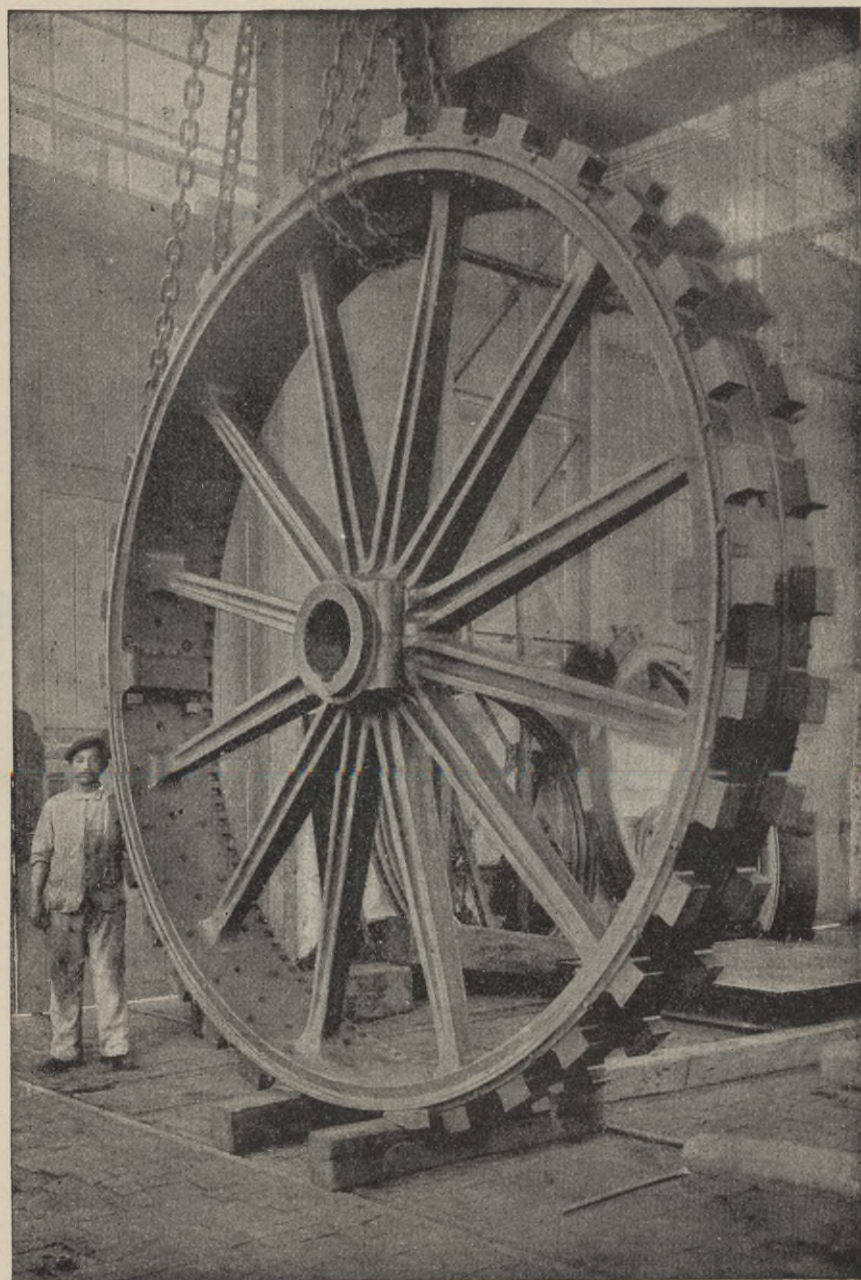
Inductorrad einer langsam laufenden Drehstrommaschine.
